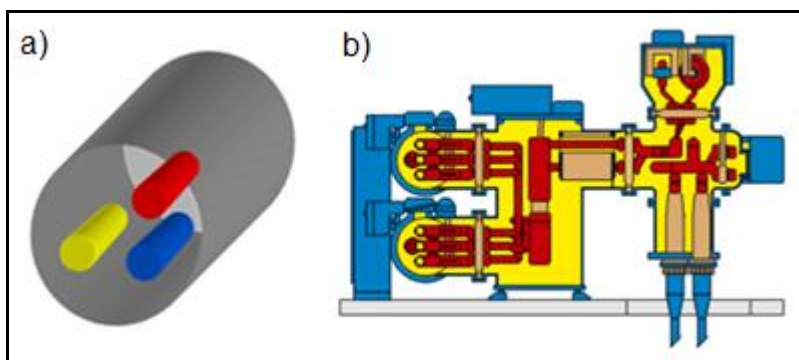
Konstrukce plynem izolovaného zapouzdrění [5].
